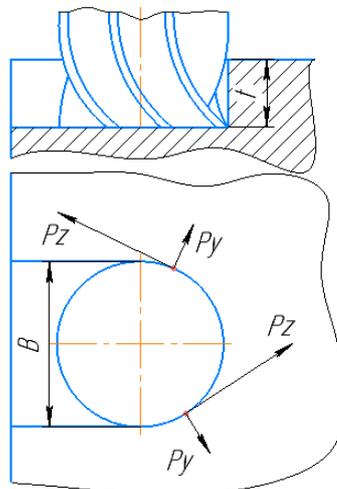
Силы резания при фрезеровании концевой фрезой
